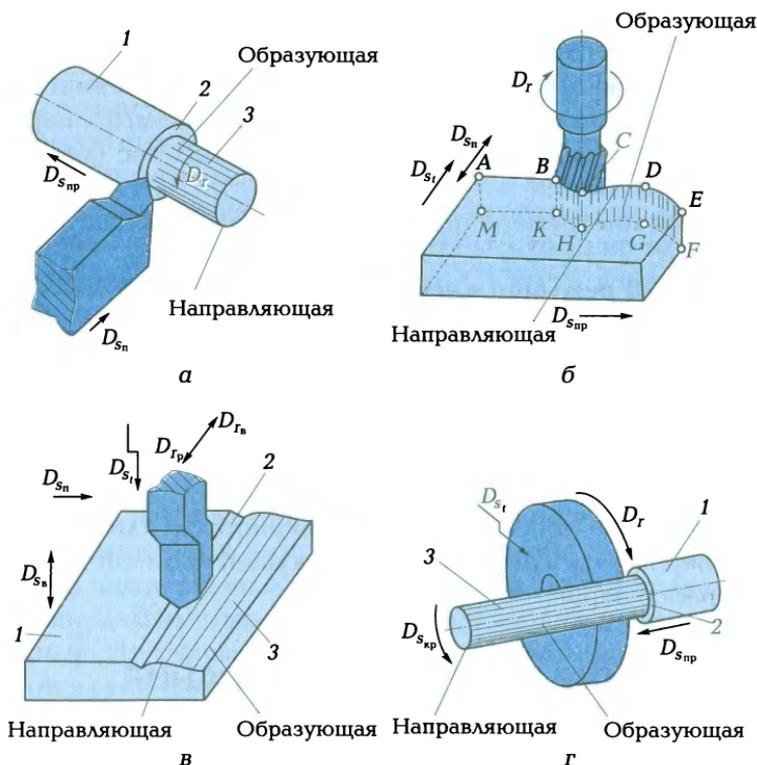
Методы обработки поверхностей заготовок резанием: а — точение; б — фрезерование; в — строгание; г — шлифование: 1 — обрабатываемая поверхность АВКМ; 2 — поверхность резания ВСНК; 3 — обработанная поверхность CDEFGH
